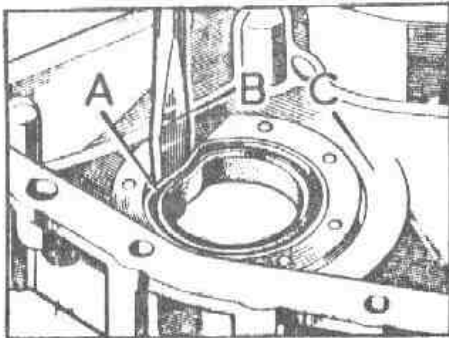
Desmontaje del retén delantero del cigueñal
